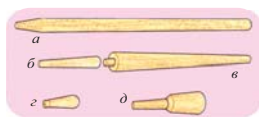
Детали цилиндрической и конической формы: а – черенок для лопаты; б – ручка для киянки; в – ножка стула; г – ручка для напильников и стамесок; д – картофелемялка
